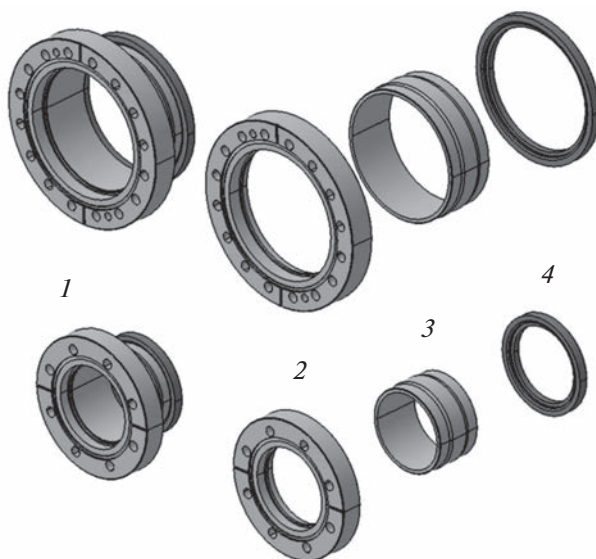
Конструкция боковых патрубков с фланцами ДУ100 (вверху) и ДУ63 (внизу): 1 – патрубок с фланцем в сборе; 2 – фланец CF (ConFlat) из нержавеющей стали; 3 – патрубок из нержавеющей стали; 4 – промежуточная медная проставка.
